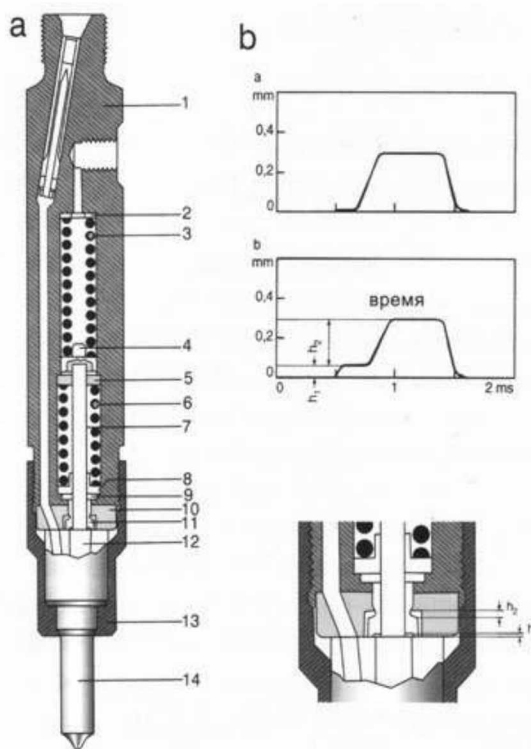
Двопружинні форсунки: 1 – корпус форсунки; 2, 9 – регулювальні шайби; 3 – потужна шайба; 4 – грибок потужної шайби; 5 – шайба, що направляє штовхач форсунки; 6 – слабка пружина; 7 – штовхач форсунки; 8 – грибок слабкої пружини; 10 – простака; 11 – опорна втулка; 12 – голка розпилювача; 13 – гайка розпилювача; 14 – розпилювач
